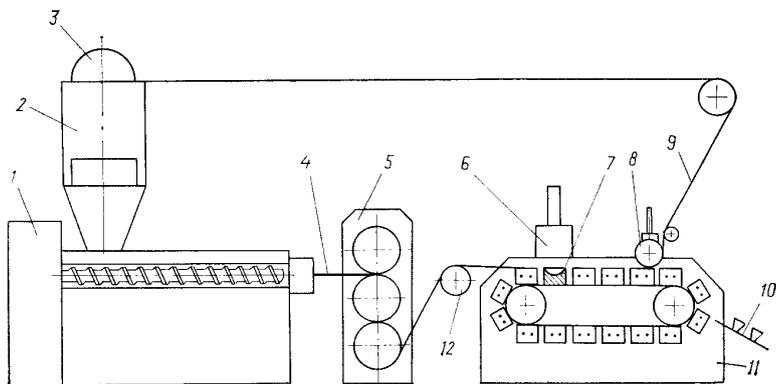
Комплексный экструзионно-формовочный агрегат:
